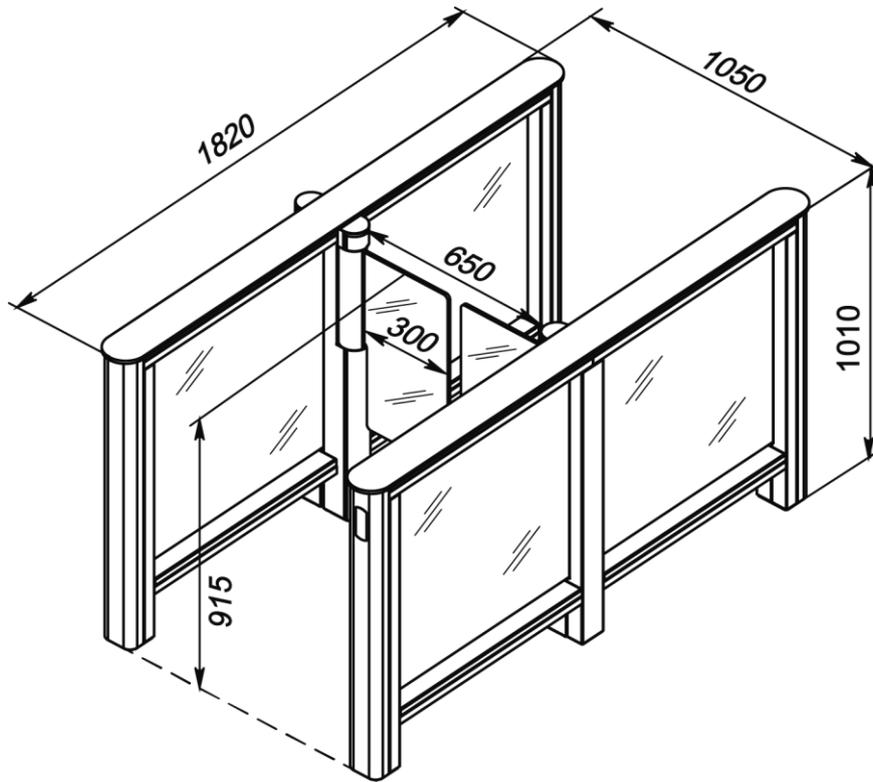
Dimensioni d'ingombro del tornello con ante ATG-300
